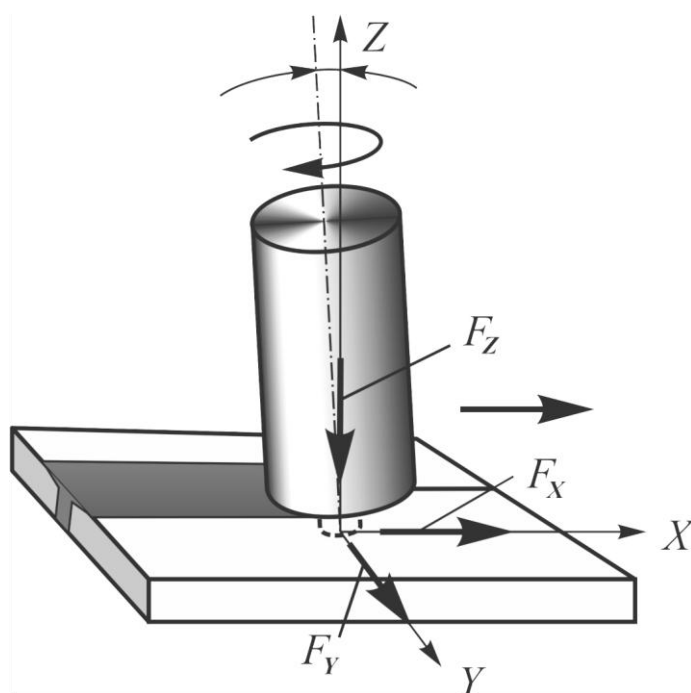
Принципиальная схема сварки трением с перемешиванием
